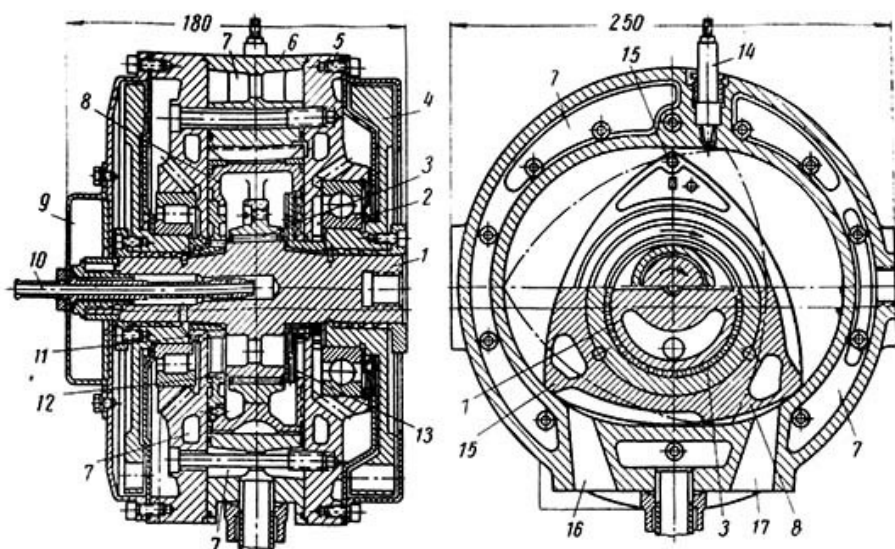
Продольный и поперечный разрезы двигателя ККМ-250:
